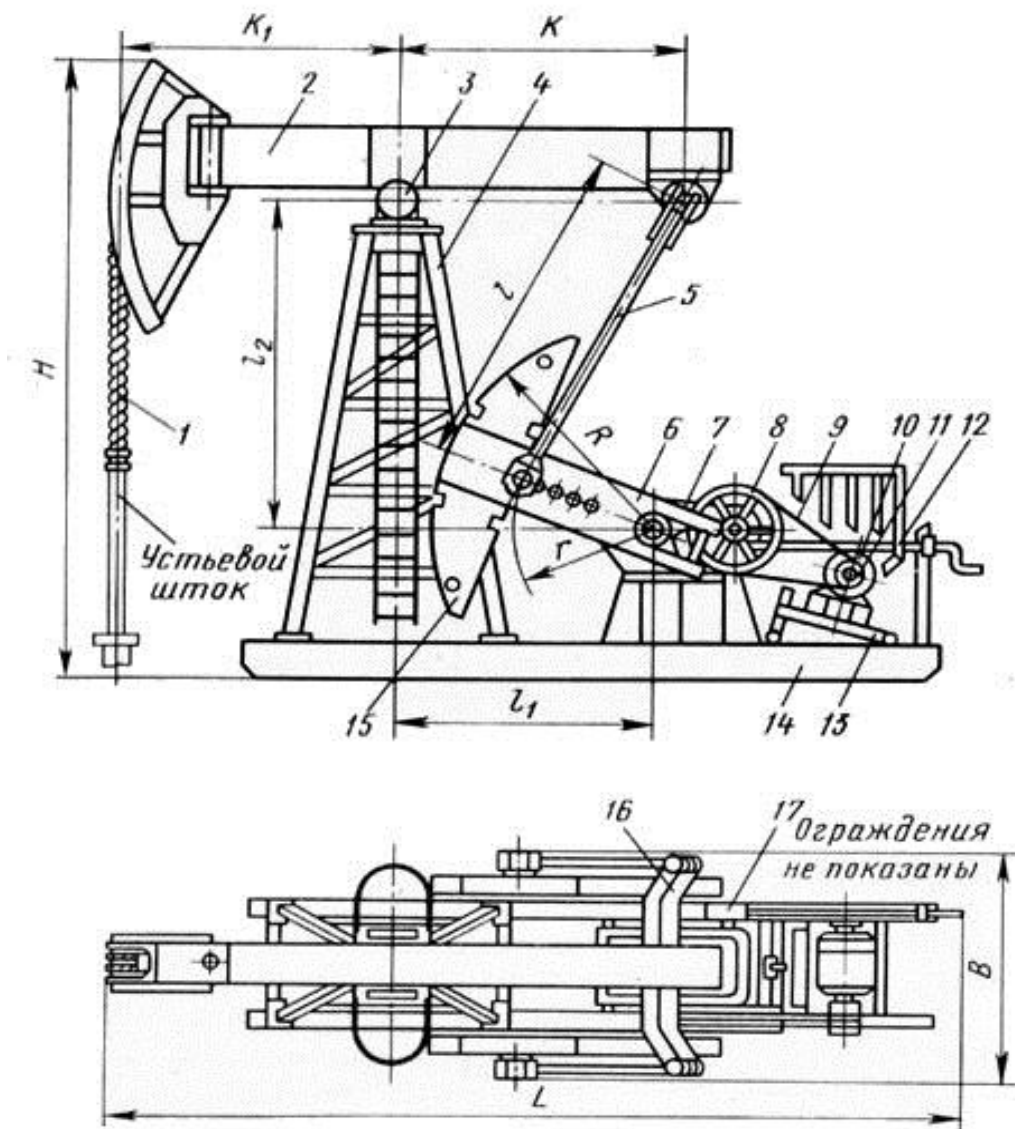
Схема балансного станка-качалки типа СКД: 1- канатная подвеска; 2-балансир с поворотной головкой; 3-опора балансира; 4- стойка; 5-шатун; 6-кривошип; 7-редуктор; 8-ведомый шкив; 9- клиноременная передача; 10-электромотор; 11-ведущий шкив; 12- ограждения; 13-саздки поворотные для электромотора; 14-рама; 15- противовес; 16-траверса; 17-тормозной шкив.
